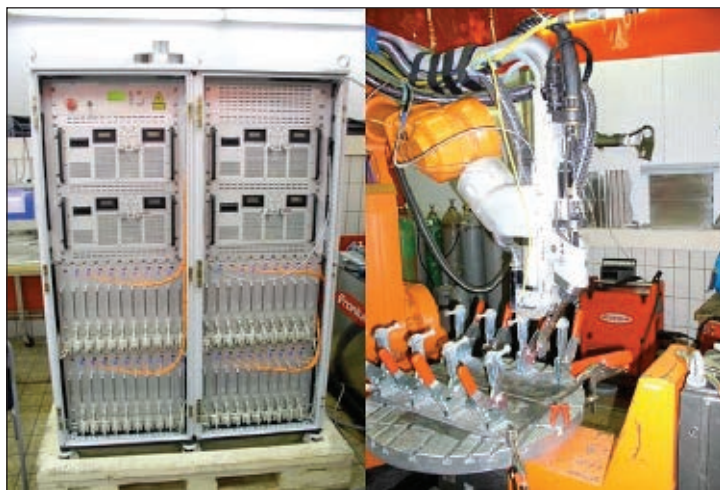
Установка гибридной лазерной сварки с волоконным лазером (мощность лазера 6,5 кВт, основной материал S235JR, присадочная проволока G3Si1)
